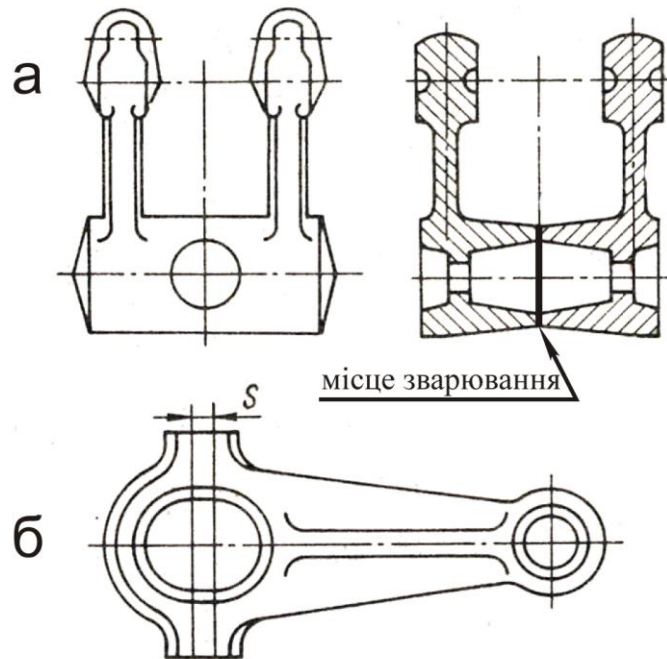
Спрощення конструкції поковки за рахунок: а – розділення на два елементи; б – об'єднання двох поковок в одну (S – ширина розрізу)
